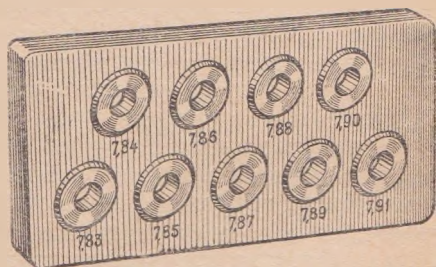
Калибровочная планка для калибровки пуль под стволы винтовок калибра 7,62 мм
